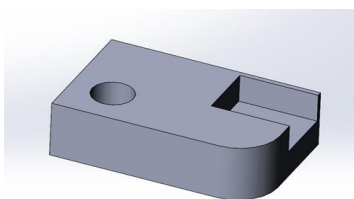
Тестова модель для перевірки точності розмірів при фрезеруванні
